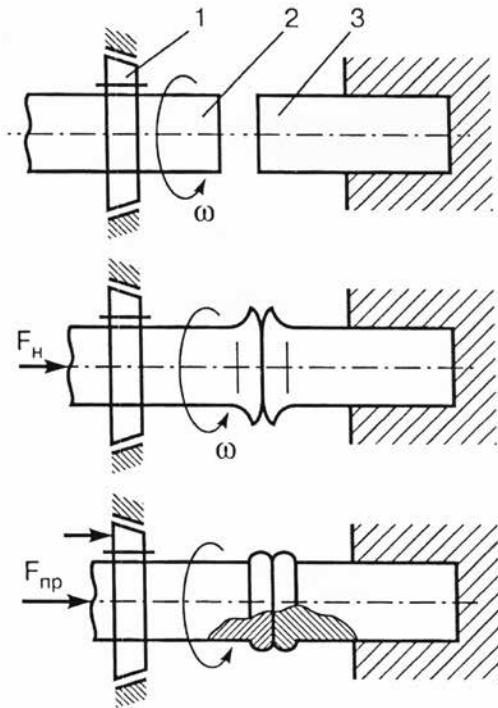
Схема конвенциональной сварки трением с непрерывным приводом: 1 – тормоз; 2, 3 – свариваемые заготовки
